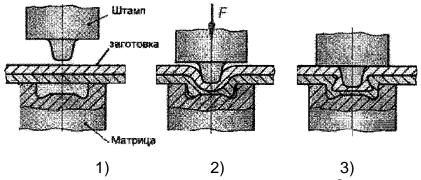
Листовая штамповка. 1,2,3 - стадии процесса
